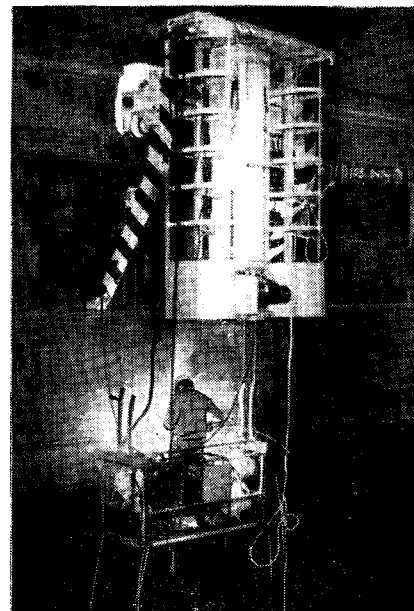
Передвижное устройство для сварки стыков наружной обшивки компании «Мицубиси хэви индастриз».
